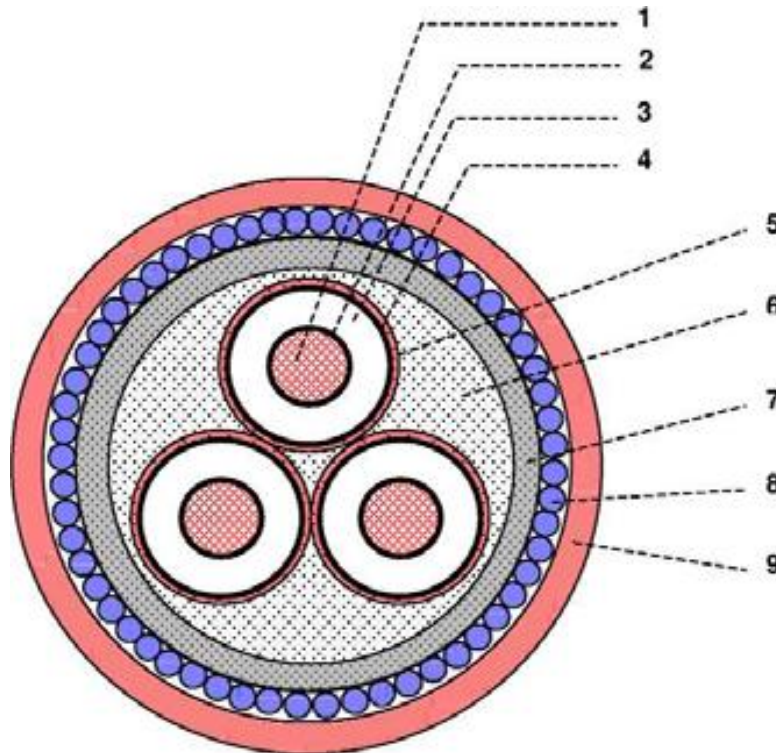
Конструкция шахтного кабеля: 1 - токопроводящая жила из меди 2-го класса гибкости; 2 – внутренний полупроводящий слой из электропроводящей резины марки ЭПШ-30; 3 – изоляция из этиленпропиленовой (ЭПР) резины; 4 - внешний полупроводящий слой из электропроводящей резины марки ЭПШ-30; 5 – экран из медных проволок; 6 – заполняющий компаунд марки RX 8053; 7- подушка из лент нетканого волокна; 8 – броня из стальных проволок; 9 – внешняя оболочка из компаунда марки V 4332-7.
